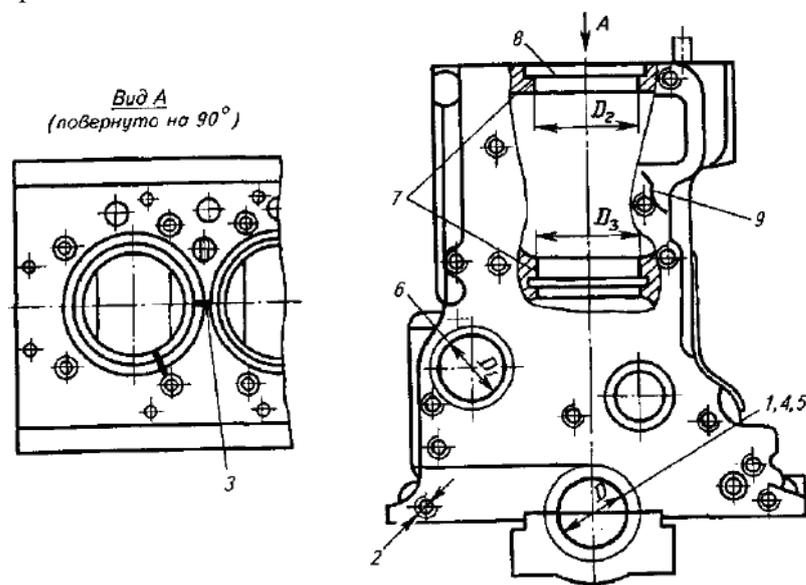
схема блока цилиндров двигателя Д-240
